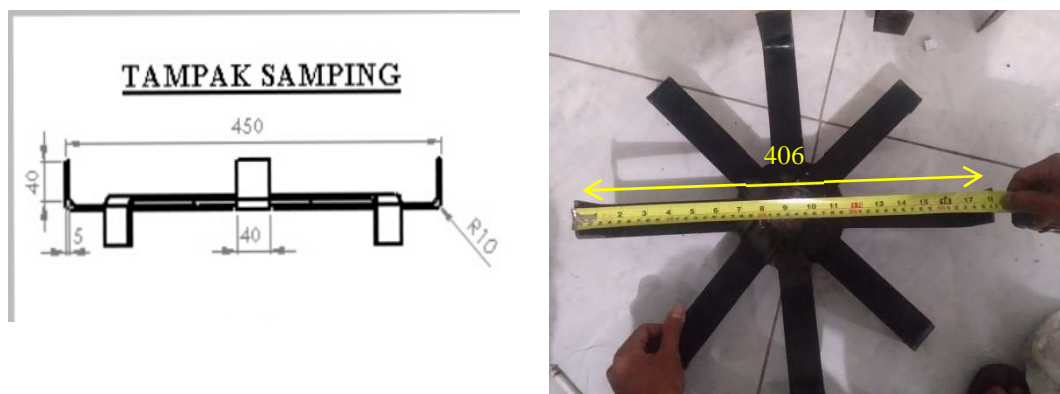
Pembengkokan Ujung Kaki Roda
